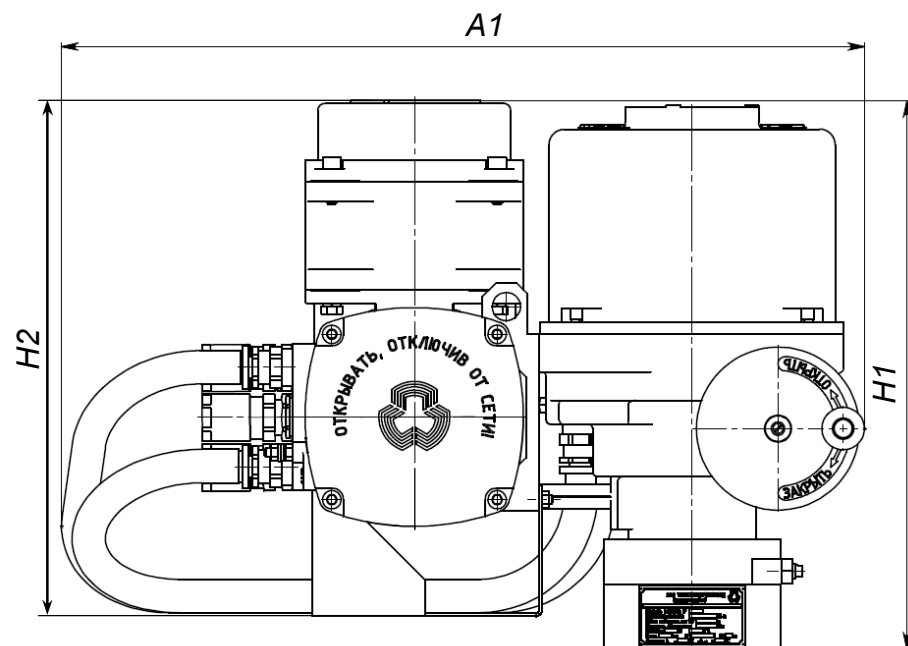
ж – Габаритные размеры привода конструктивных схем 1, 11, 12 с блоком управления ВЭЗ
